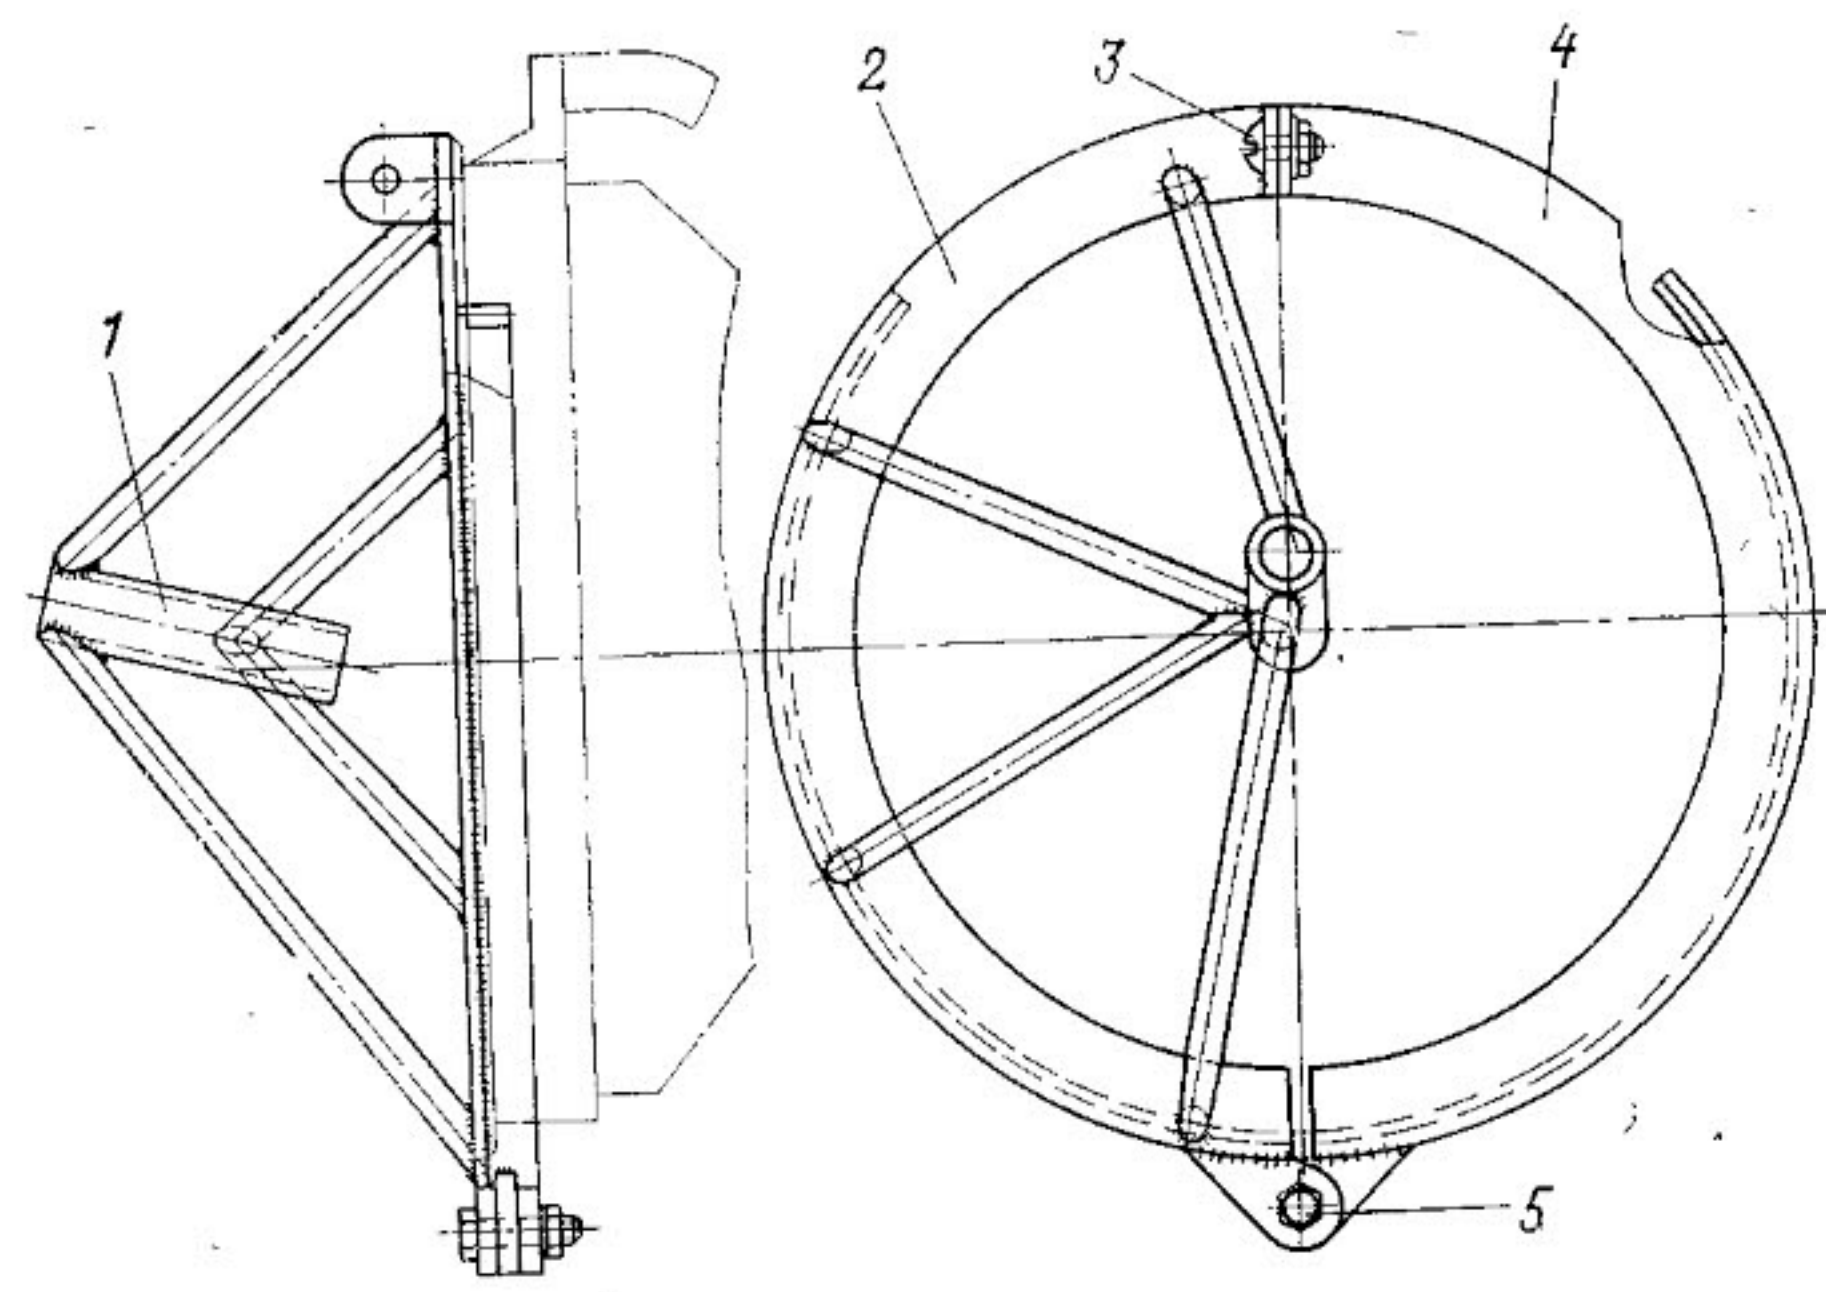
Приспособление для установки трубки холодной пристрелки при регулировке фар:
